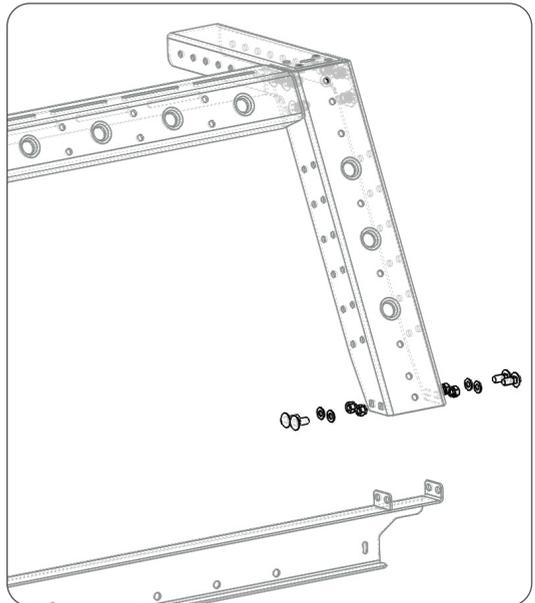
Detailansicht des verschraubten unteren Rahmens / detailed view of bolted down lower frame
